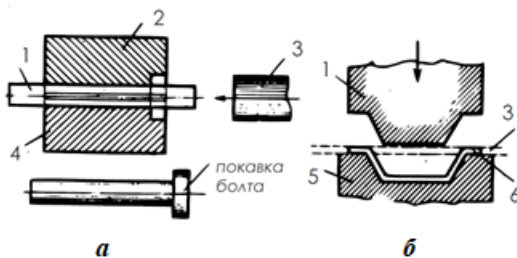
Операції штампування: *а – схема штампування заготовки болта; б – схема роботи згинального штампа; 1 – заготовка; 2 – рухома частина матриці; 3 – пуансон; 4 – нерухома частина матриці; 5 – матриця; 6 – готовий виріб.
